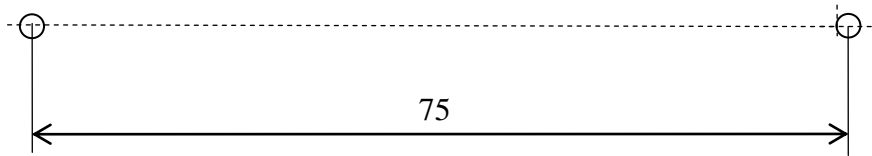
Разметка крепления корпуса УПВК-0,3П
